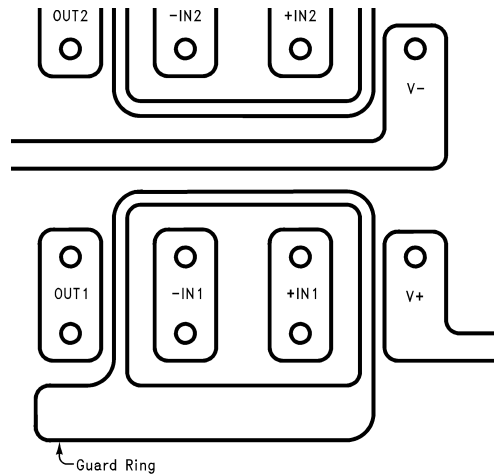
防护环的 PCB 布局典型连接中的防护环示例
